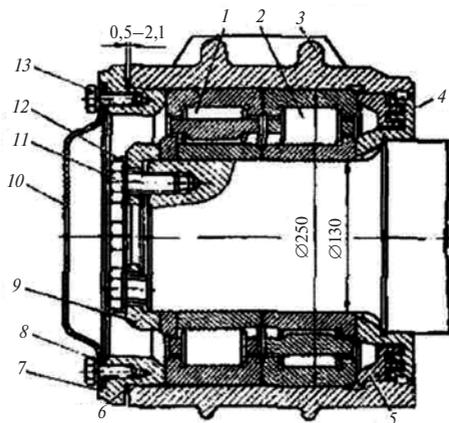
Букса грузового вагона с торцевым креплением цилиндрических роликовых подшипников тарельчатой шайбой:
